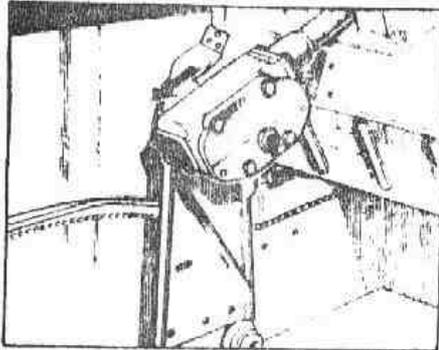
Desmontaje del conjunto de la caja de dirección y de los soportes
